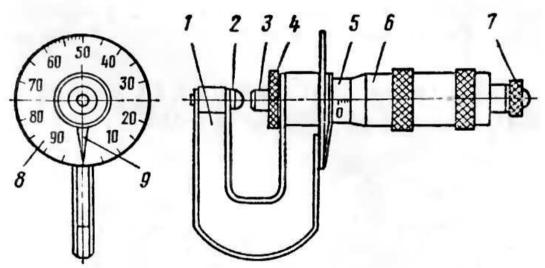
Общее устройство микрометра с циферблатом: 1 – скоба; 2 – пятка; 3 – микрометрический винт; 4 – стопор; 5 – стебель; 6 – барабан; 7 – трещотка; 8 – циферблат; 9 – стрелка
